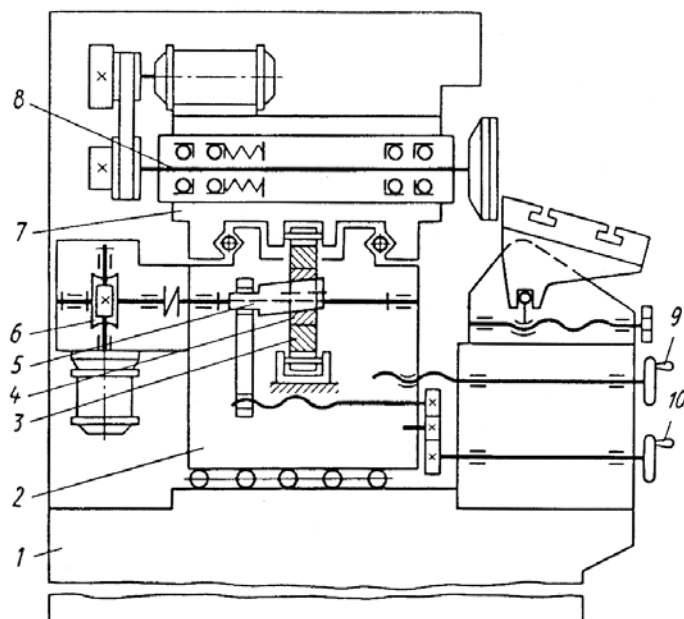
Кинематическая схема станка мод. 3622 для заточки резцов:
